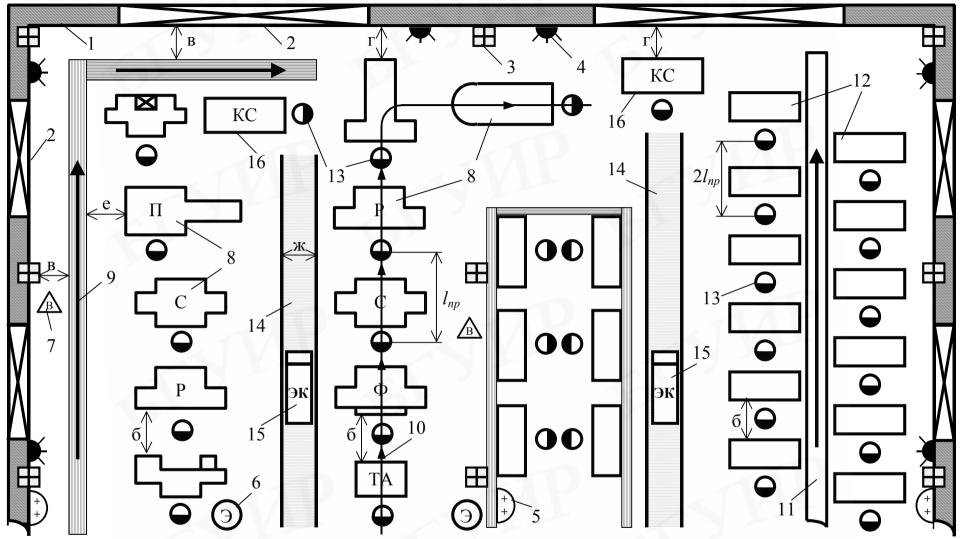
Планировка участка механообрабатывающего цеха:
